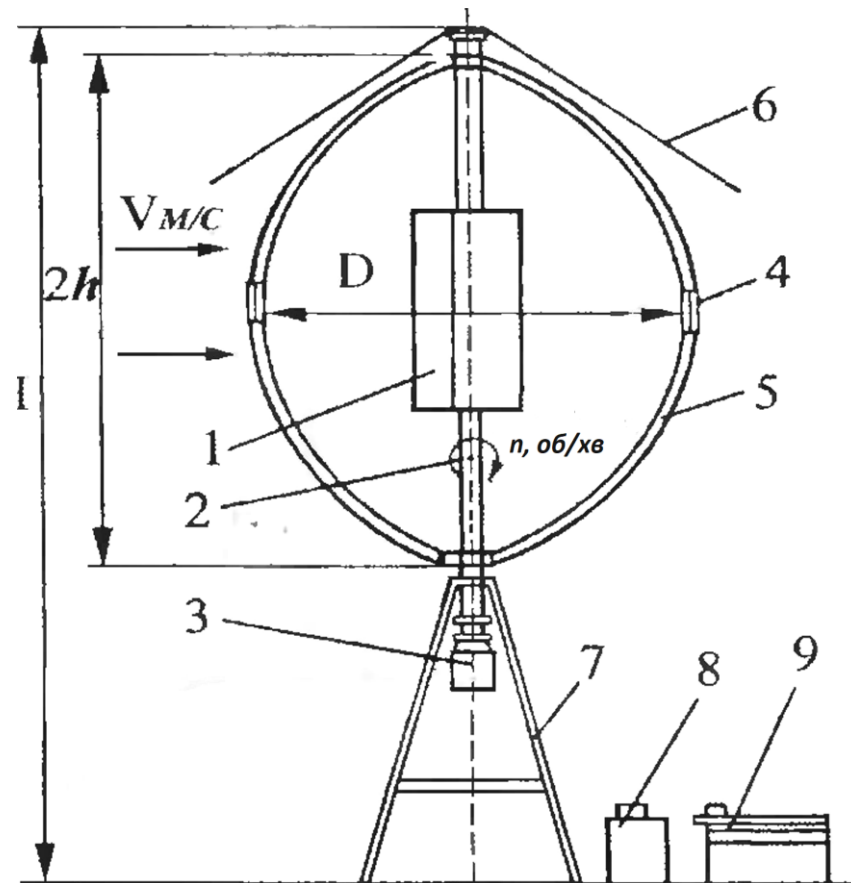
Конструктивна схема ВЕУ з вертикальною віссю обертання типу «Дар'є»: 1 – стартер (ротор Савоніуса); 2 – вал; 3 – електрогенератор; 4 – гальмівний пристрій; 5 – робоча лопасть; 6 – розтяжки; 7 – рама; 8 – перетворювач напруги; 9 – акумулятор.
